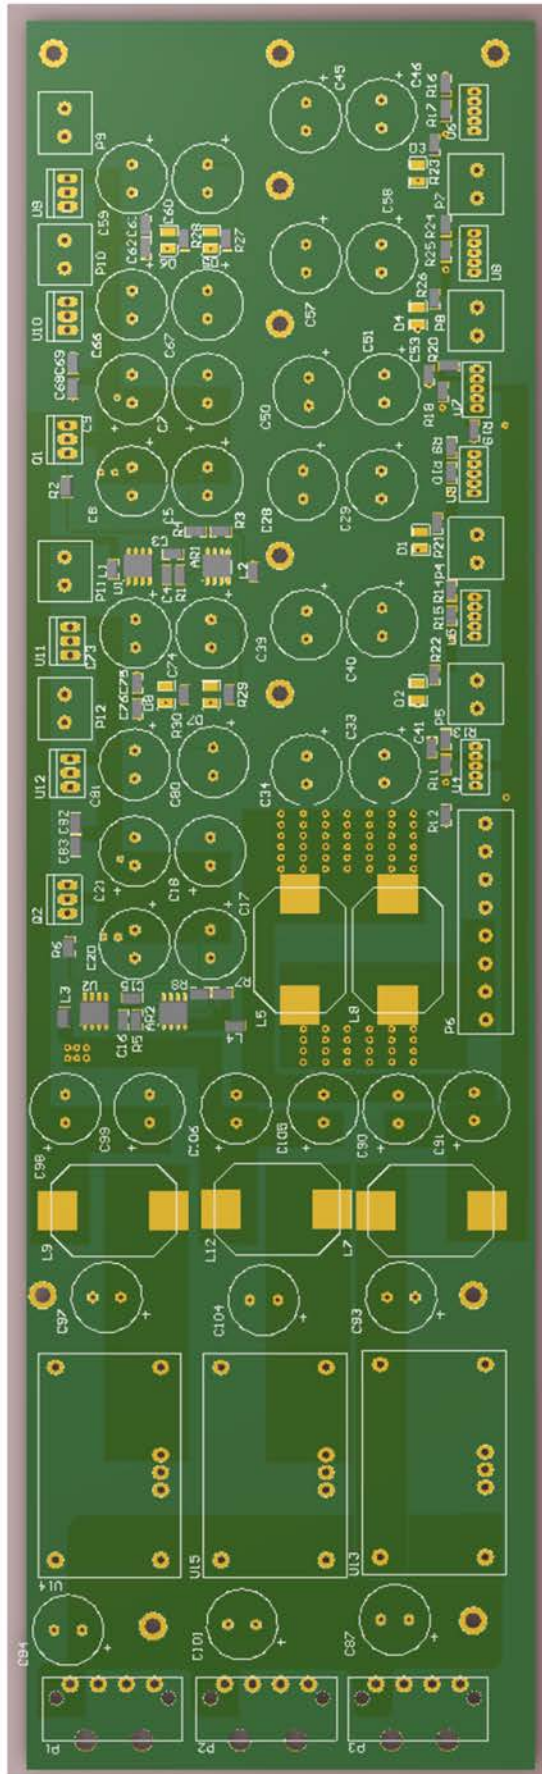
34: PCB dell'alimentatore lineare (top).
